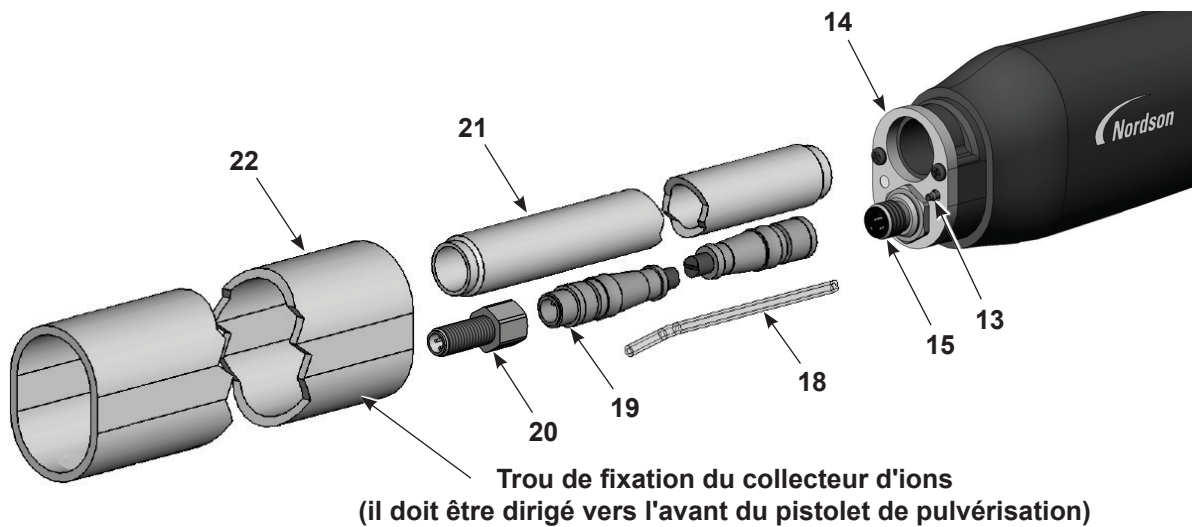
Démontage du pistolet à fixation sur tube 2 sur 5
